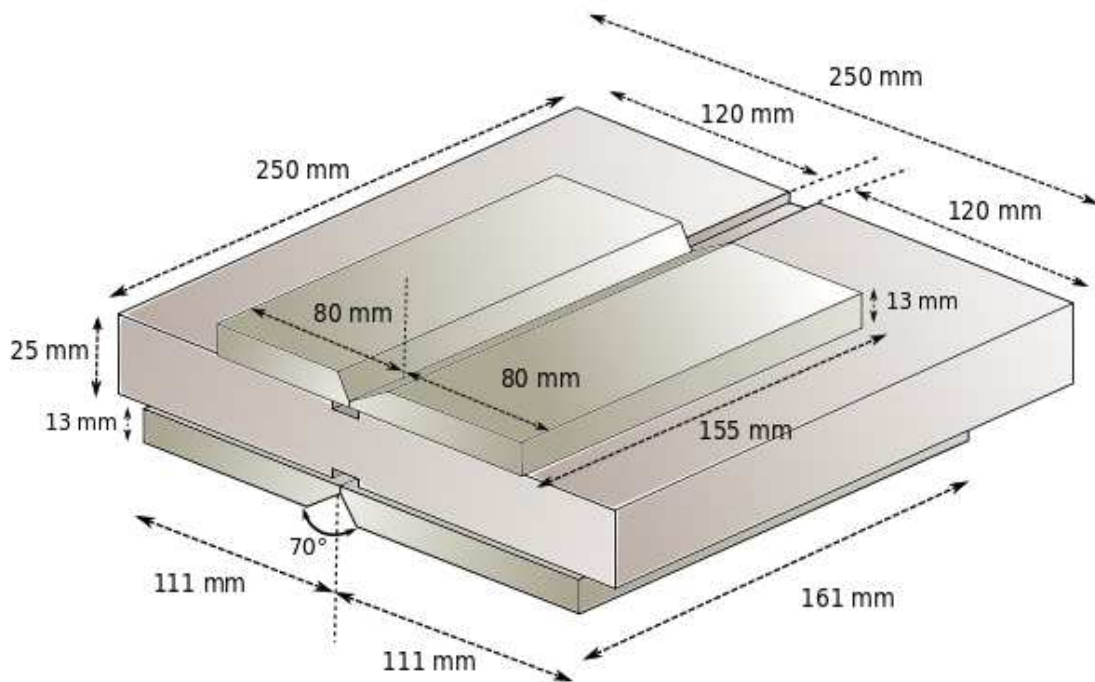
Corpos de prova do Aço Inoxidável Duplex 2205 fixadas na chapa de aço carbono para o processo de soldagem GTAW.
